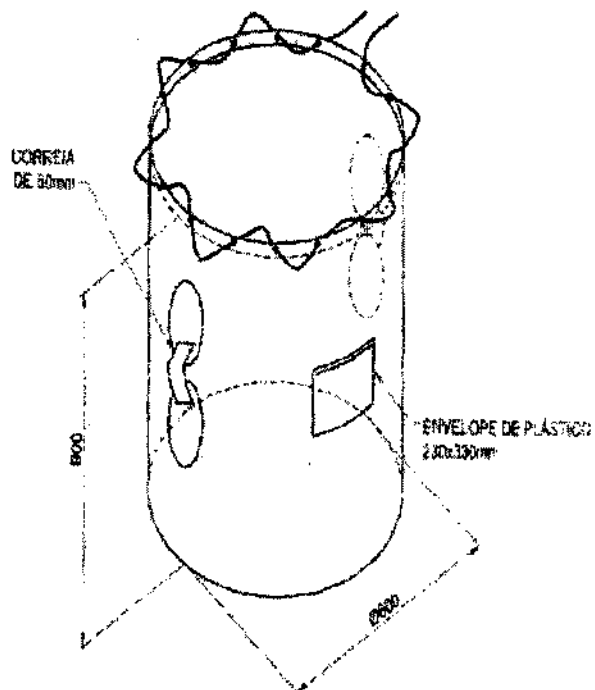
Bolsa para do forro térmico da barraca (medidas em mm)
